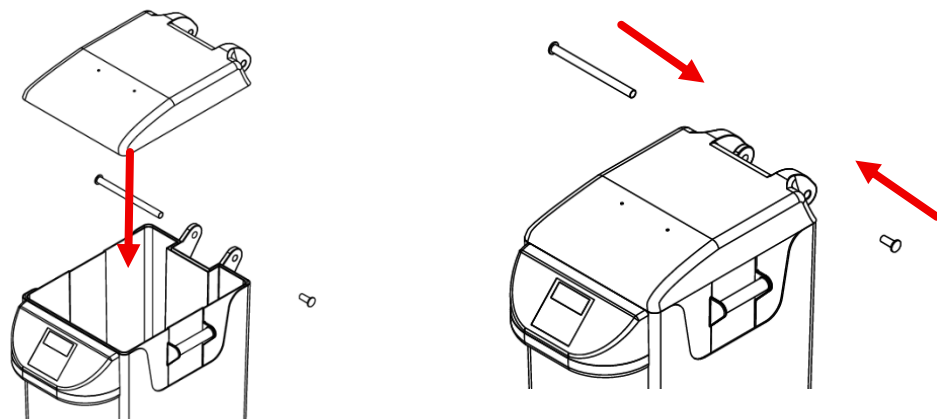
Montaje de la tapa. Fuente: Primaria.
